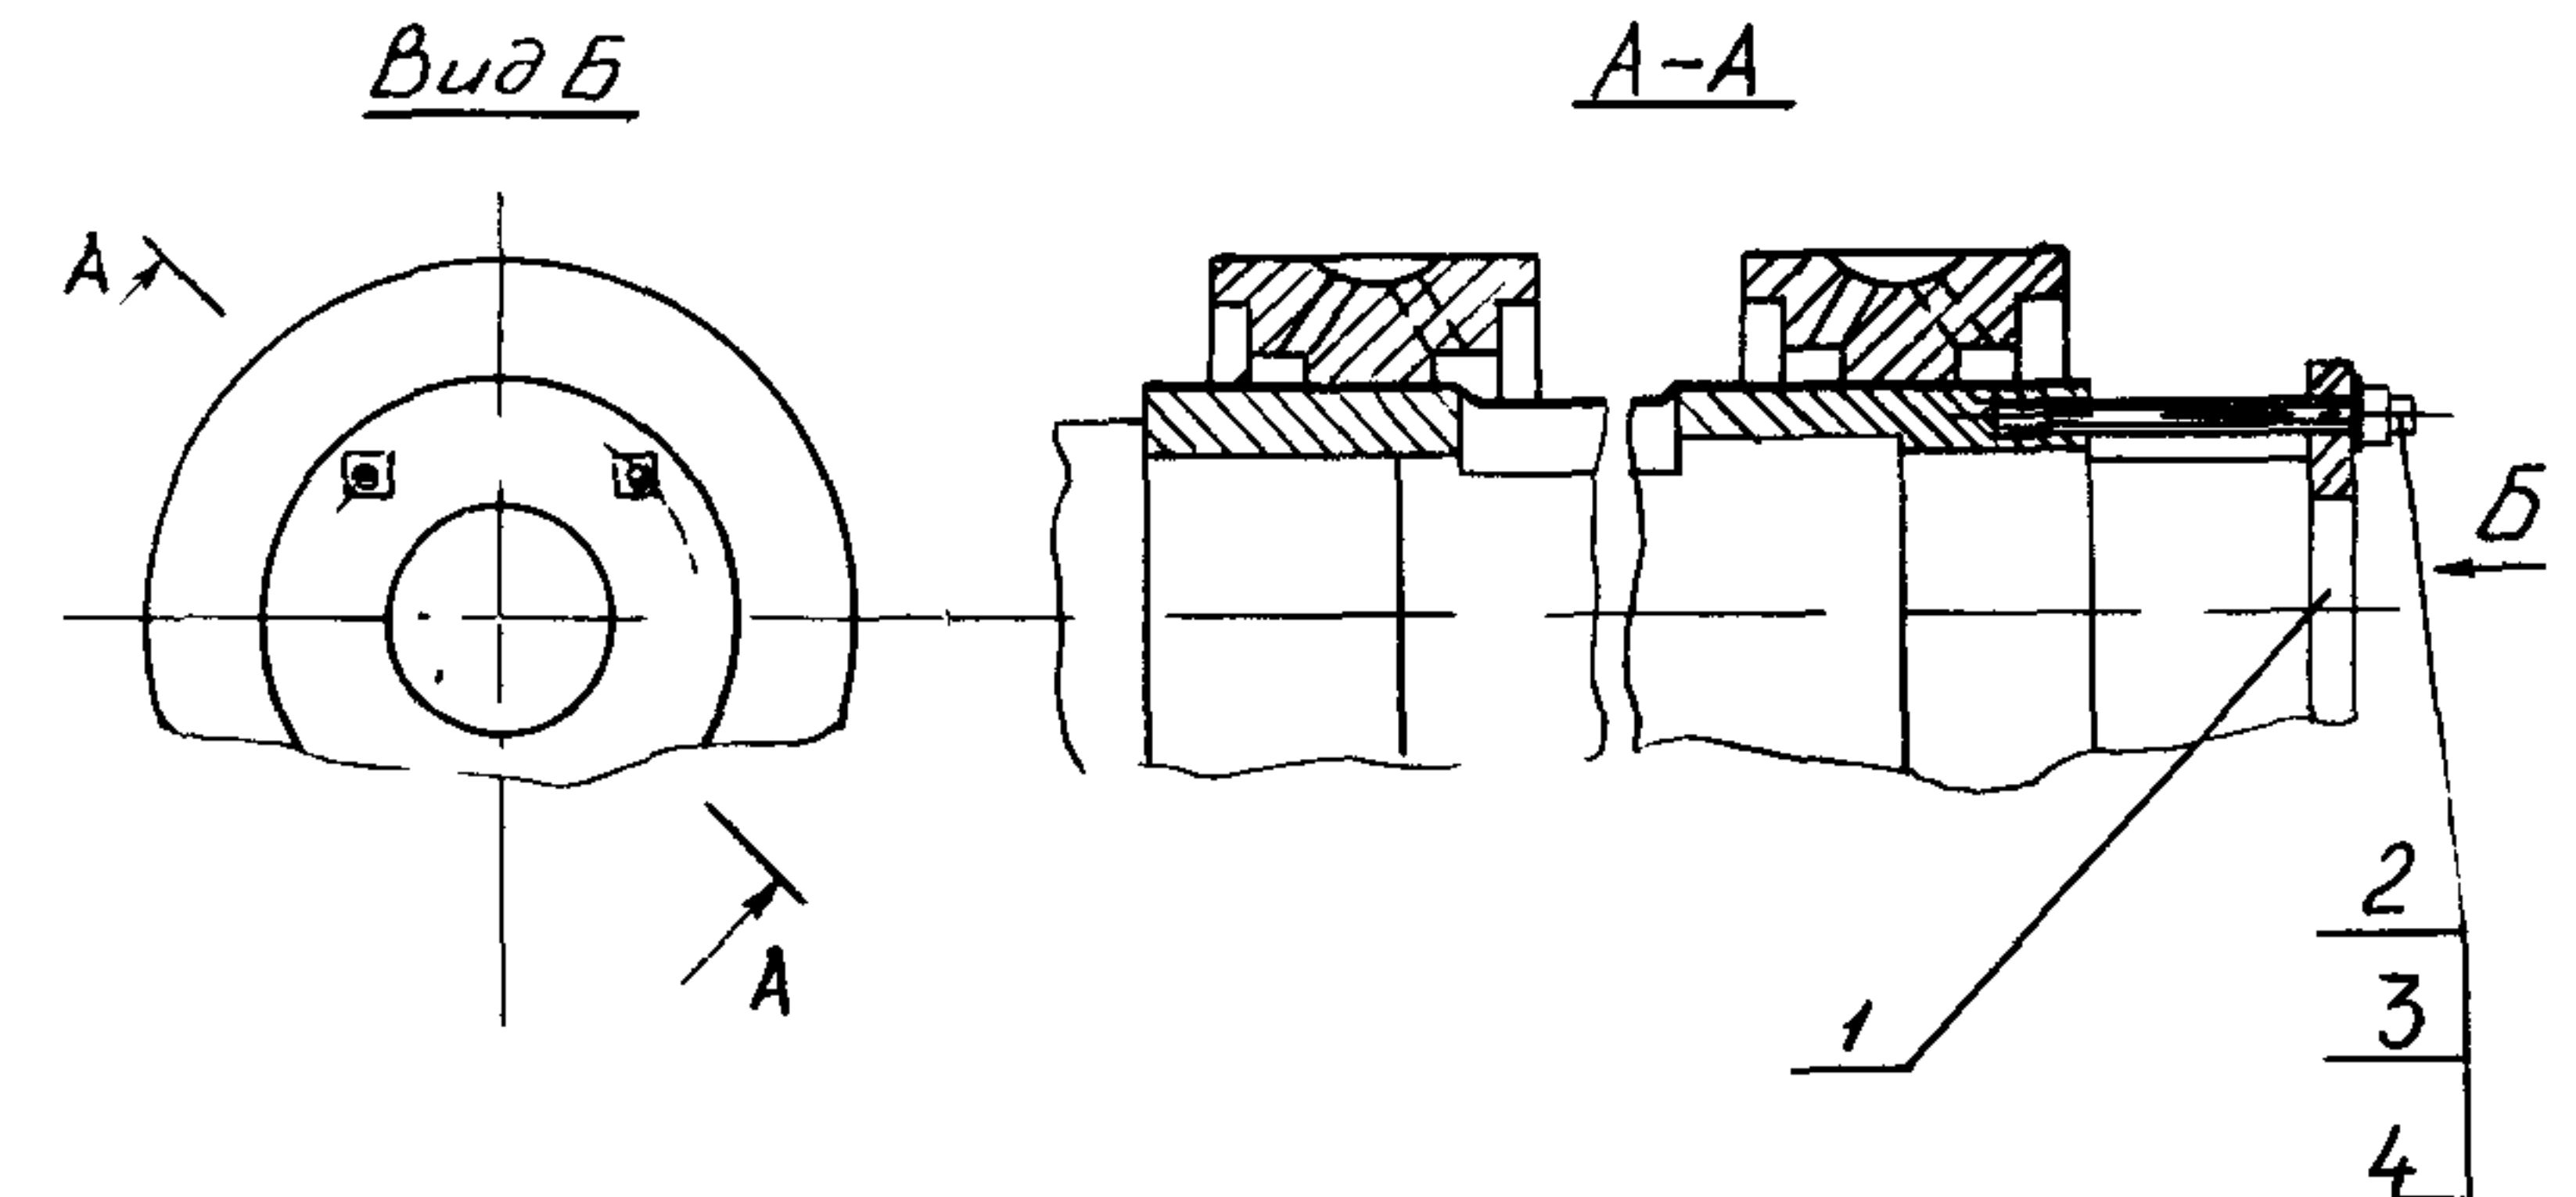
Приспособление для снятия контактных колец: 1 - кольцо; 2 - шпилька стяжная; 3 - гайка; 4 - шайба
